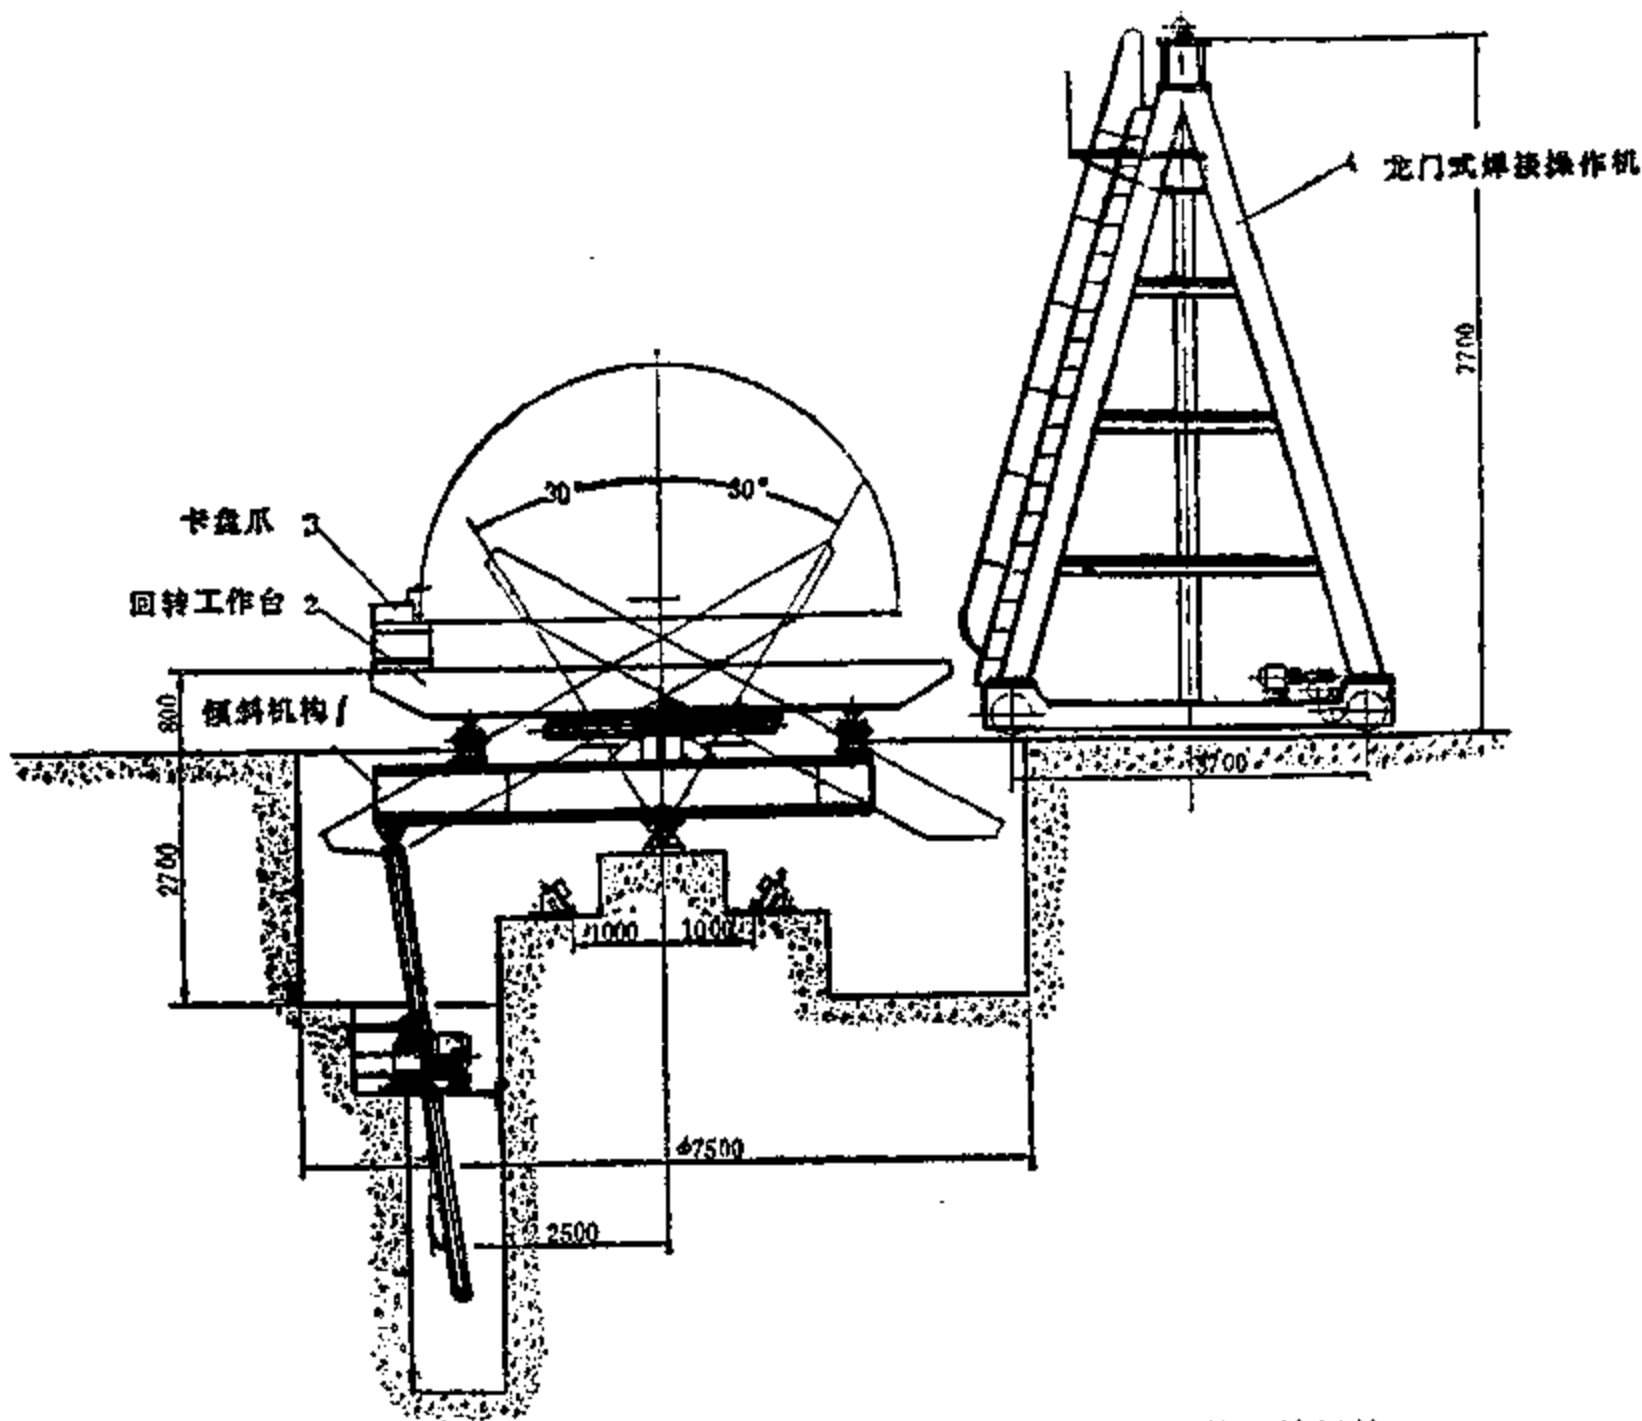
用横梁可升降的门式焊接架进行外环缝焊接
